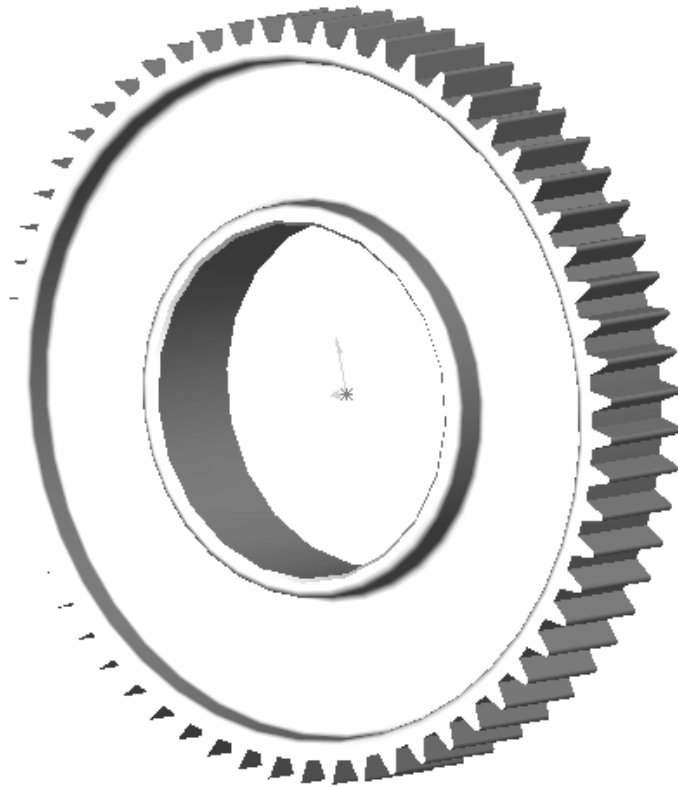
Пример трехмерной модели зубчатого колеса
